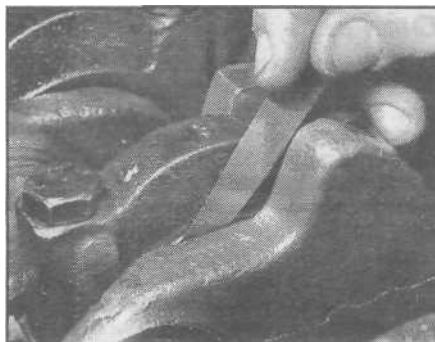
Проверка осевого люфта коленчатого вала на коренном подшипнике № 3
